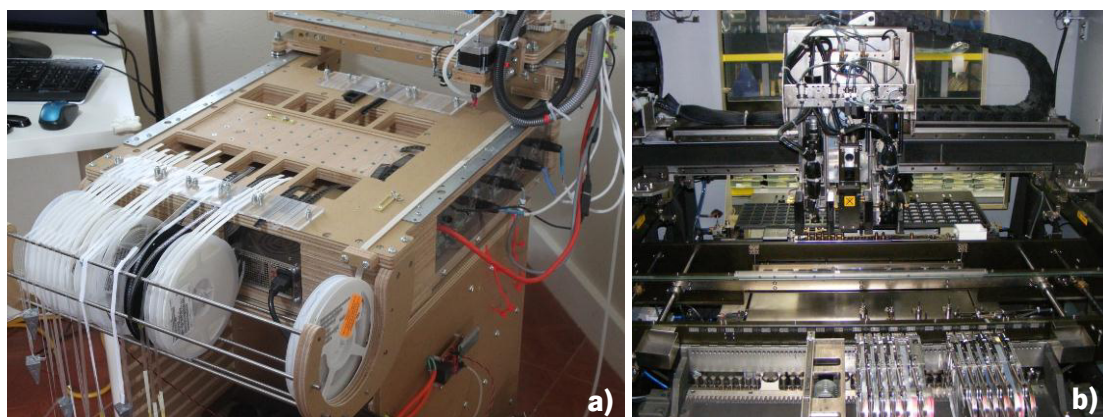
a) Mesa de alimentação [18], b) Pick and Place [19]
